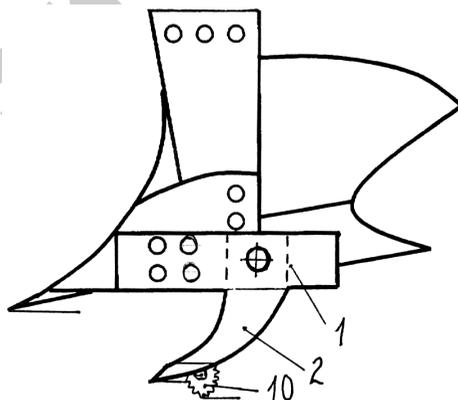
Общий вид корпуса плуга (вид сбоку)
